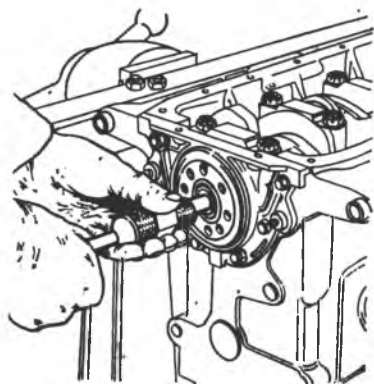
Выпрессовка подшипника вала коробки передач из коленчатого вала выталкивателем А.40006/1 в цанговым наконечником А.40006/3
